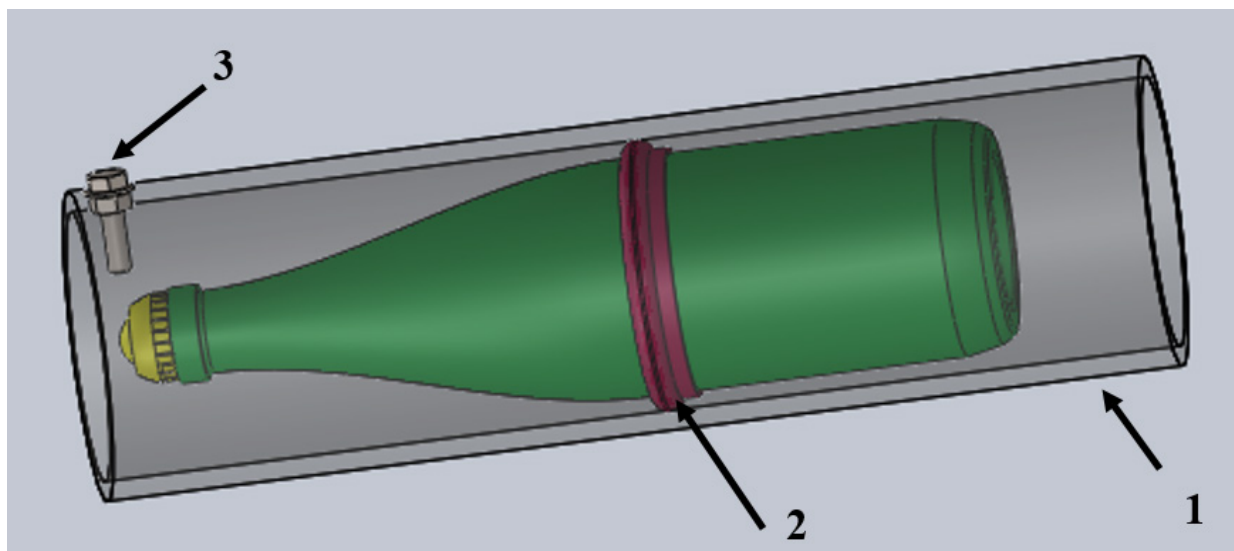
Корпус стенда (1 — корпус, 2 — кольцо, 3 — предохранительный болт)
